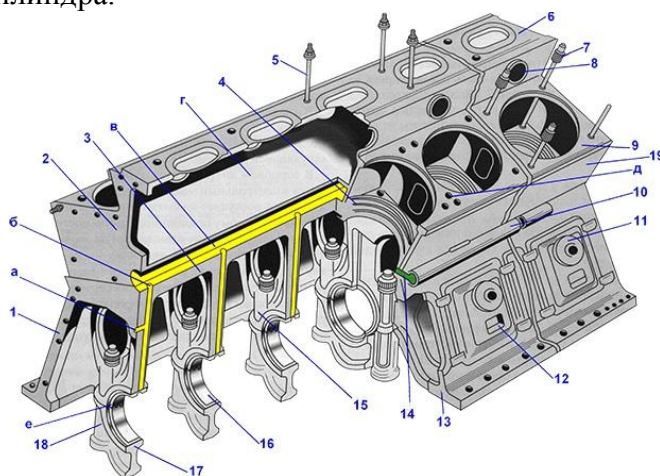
Блок цилиндров тепловозного дизеля типа Д49: 1 - корпус блока; 2 - передний лист блока; 3 - средняя плита; 4 - проставочная втулка; 5 - шпилька крепления лотка; 6 - верхняя плита; 7 - шпилька крепления цилиндровых крышек; 8 - проставок для подвода воздуха к впускным клапанам; 9 - верхний лист блока цилиндров; 10 - водяной коллектор; 11 - предохранительный клапан; 12 - крышка люка картера; 13, 15 - стойка блока; 14 - втулки из нержавеющей стали для перепуска воды из коллекторов к рубашкам цилиндров; 16 - вкладыши коренных подшипников; 17 - подвеска; 18 - болт; 19 - боковые продольные листы блока; а, б, в - маслоподводящие каналы; г - воздушный коллектор; д - отверстие для перепуска масла из крышки в картер дизеля; е - фиксирующие зубцы стыка подвески.
